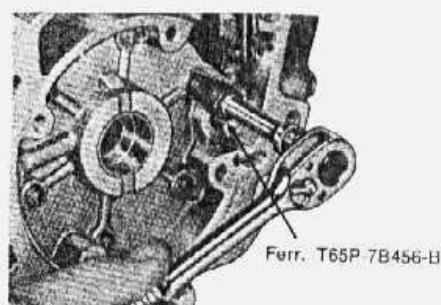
remoção dos parafusos de fixação da pista externa da embreagem uni-direcional
